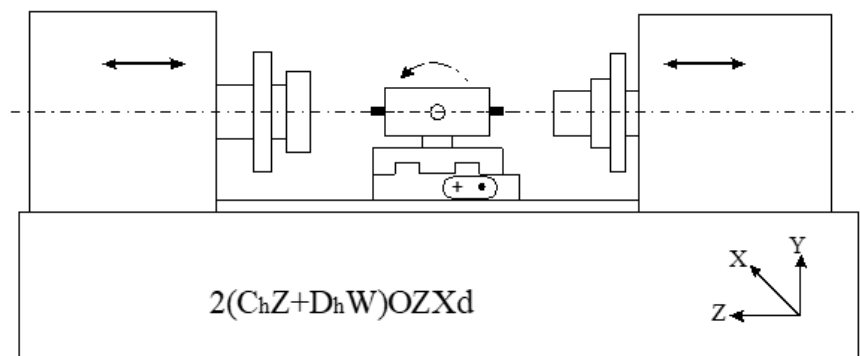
Компонування верстату з рухомими шпindelними бабками
